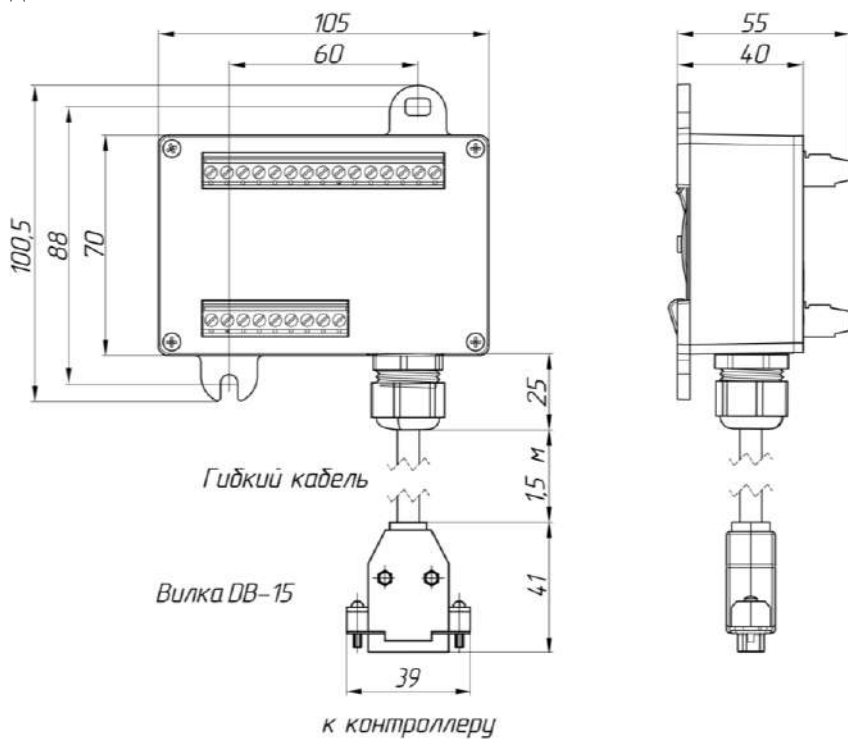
Внешний вид коробки клеммной: код вида 25
